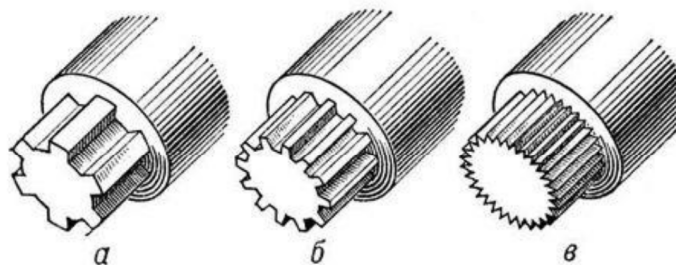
Виды шлицевых соединений: прямобочные, эвольвентные, треугольные.
